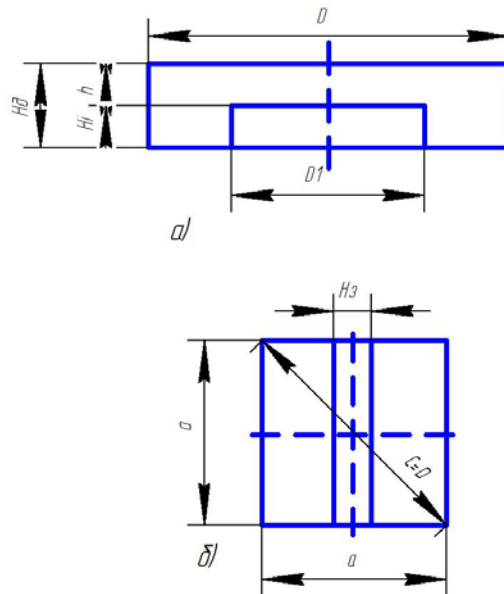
Розміри готової деталі (а) і вихідної заготовки (б)
